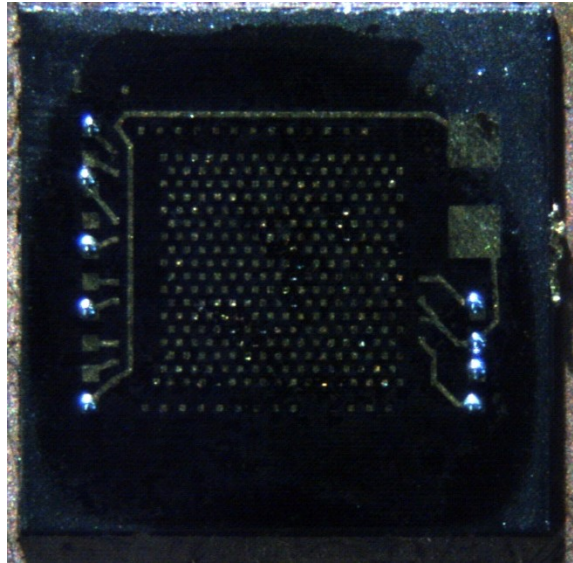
Placement des billes de soudure sur le substrat de diamant
